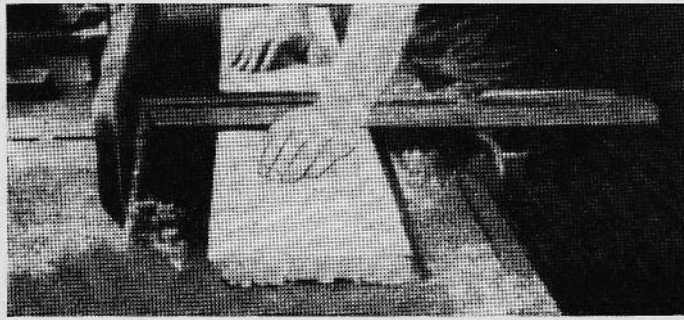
Das schwache Werkstück wird unter dem Messerschutz durchgeführt
